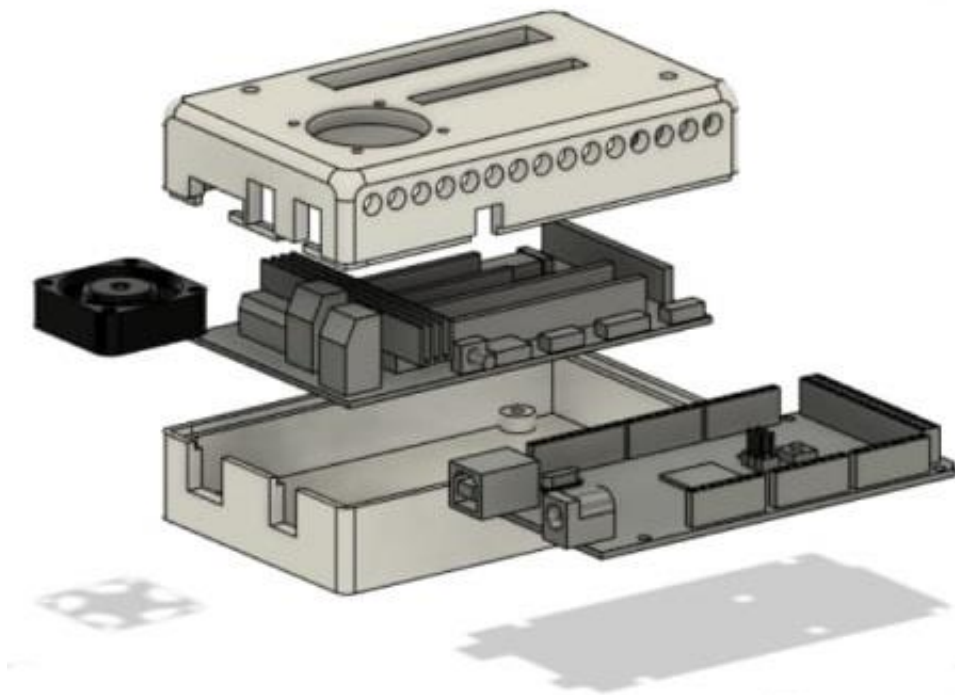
«Вибух-схема» корпусу системи керування верстатом
